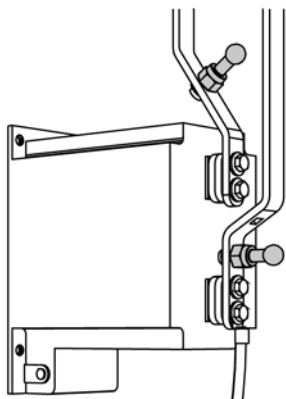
Заземляющая шпилька для ячейки типа сборная шина-сборная шина
